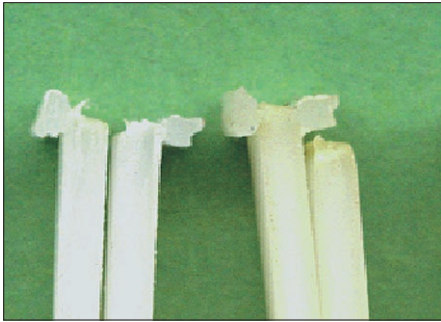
Bruchbild Schweißung Serie 3 , HS, Suspensionstyp
